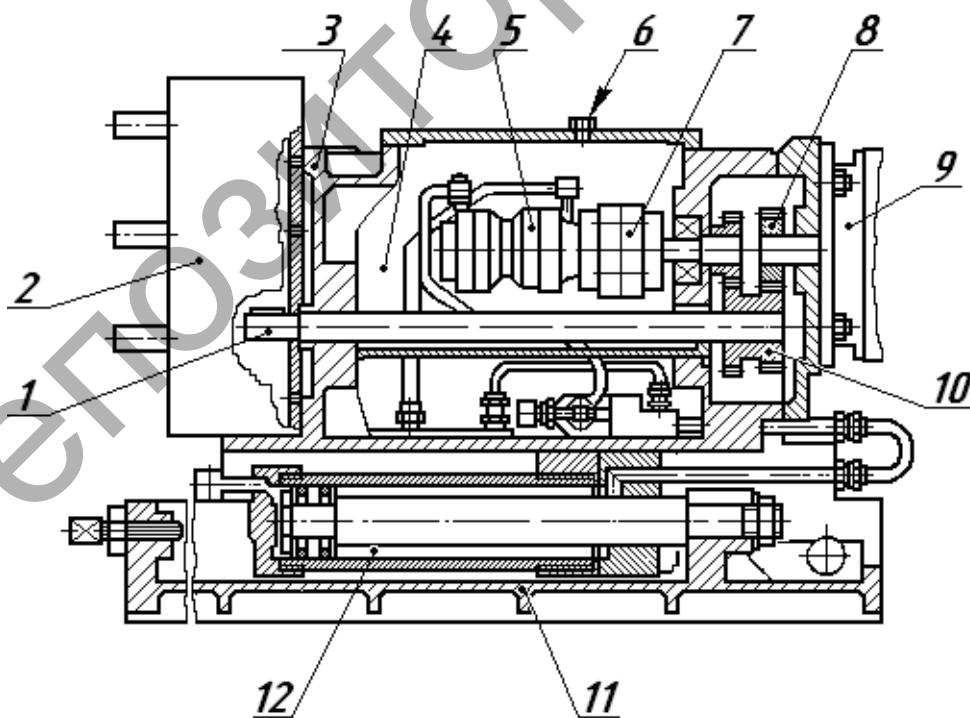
Конструктивный разрез многошпиндельной силовой головки
